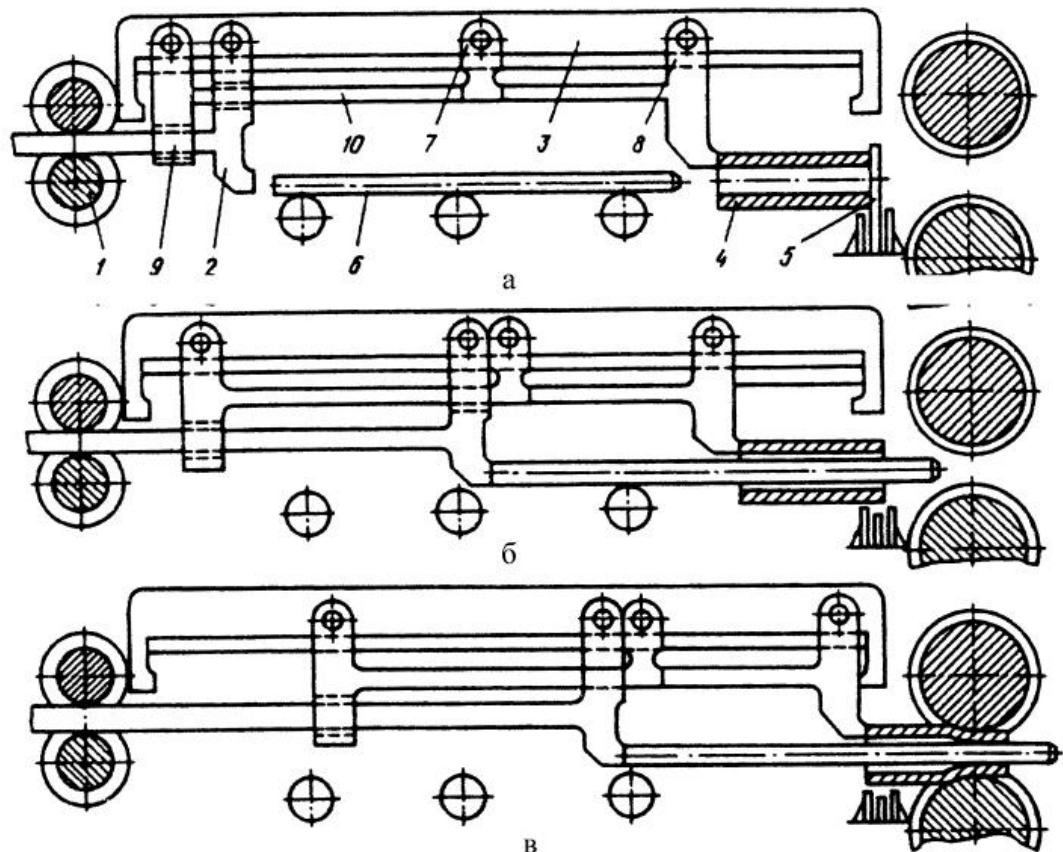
Схема устаткування для введення оправки в гільзу і подачі її в прокатні валки: 1 – ролики; 2 – каретка; 3 – напрямна; 4 – гільза; 5 – упор; 6 – оправка; 7 – упор; 8 – каретка; 9 – каретка; 10 – напрямна
